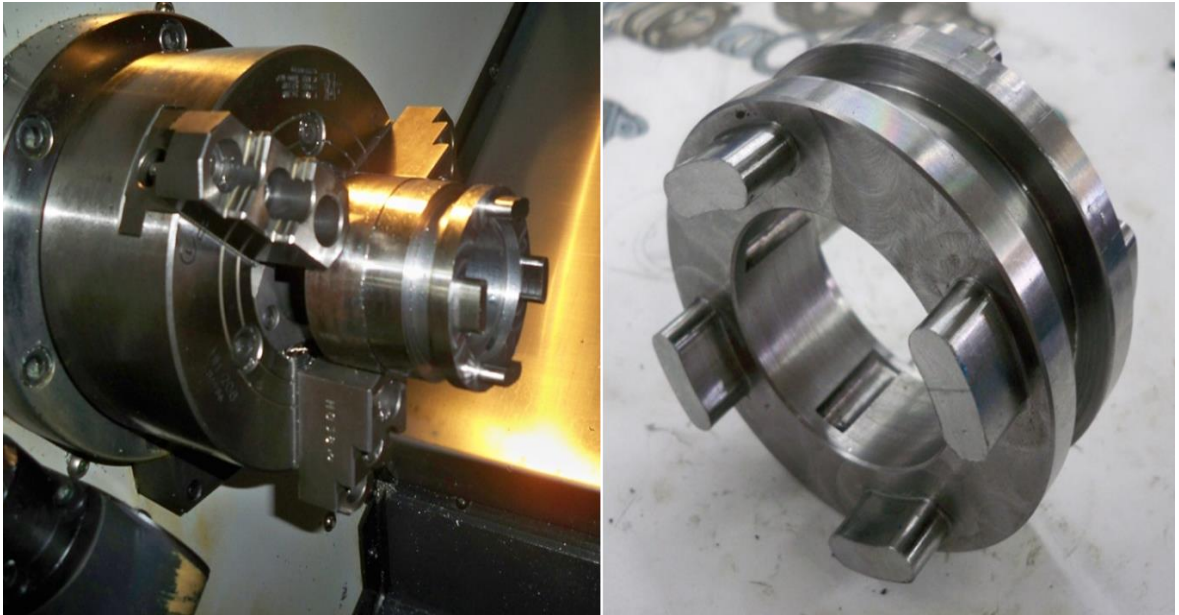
Maquinado de los engranajes. (Uso de fresadora convencional y torno CNC)
